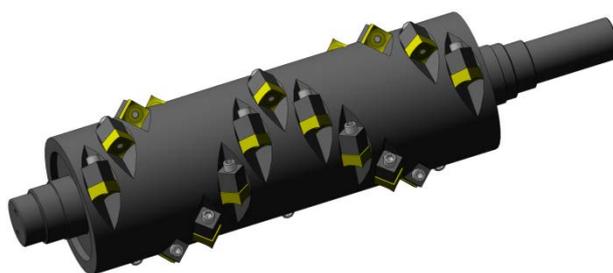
3D-модель сборочной единицы «Ротор» из сборки «Корпус шредера»
